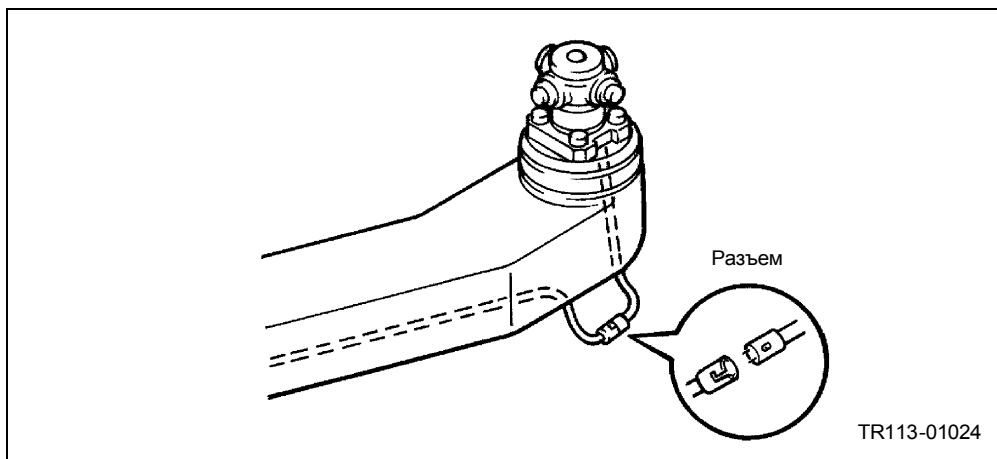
Замените датчик TOOL EYE (3/4)
